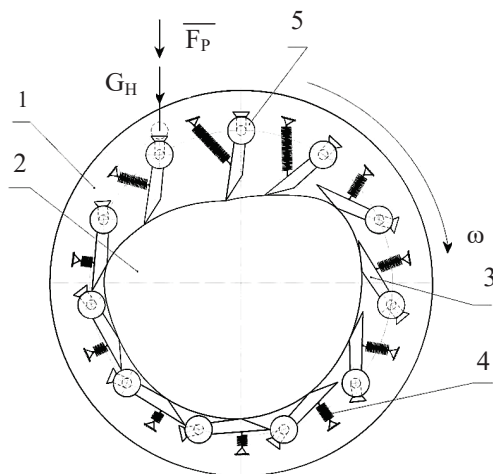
Схема дозуючого диска з дозатором направленої дії: 1 — висівний диск; 2 — нерухомий копір; 3 — важіль; 4 — пружина; 5 — поворотна комірка
